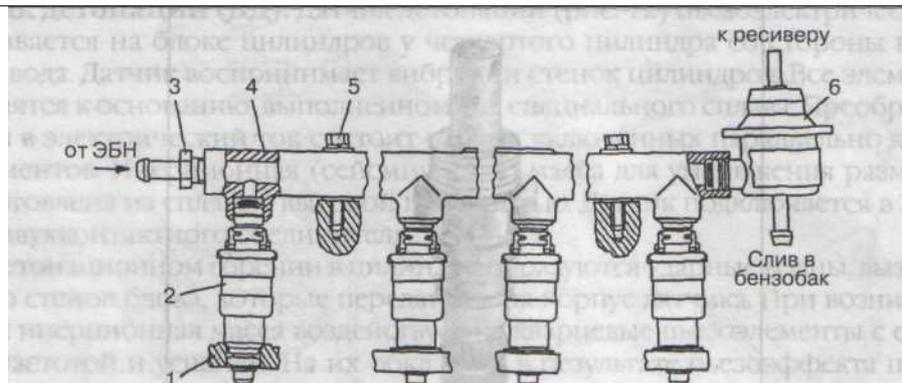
Рампа: 1 - впускная труба; 2 - форсунка; 3 - штуцер; 4 - топливопровод (рампа); 5 - болт крепления рампы; 6 - регулятор давления топлива (РДТ)
